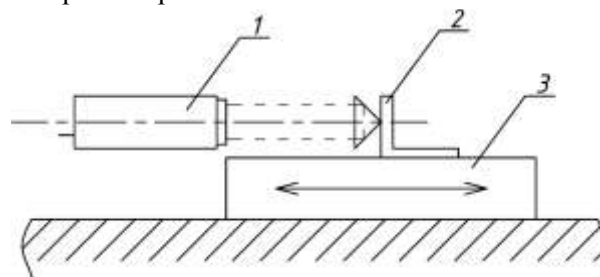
Схема контролю прямолінійності переміщень робочих вузлів верстата з використанням лазера: 1 – лазер; 2 – фотоприймач; 3 – контрольований робочий вузол
